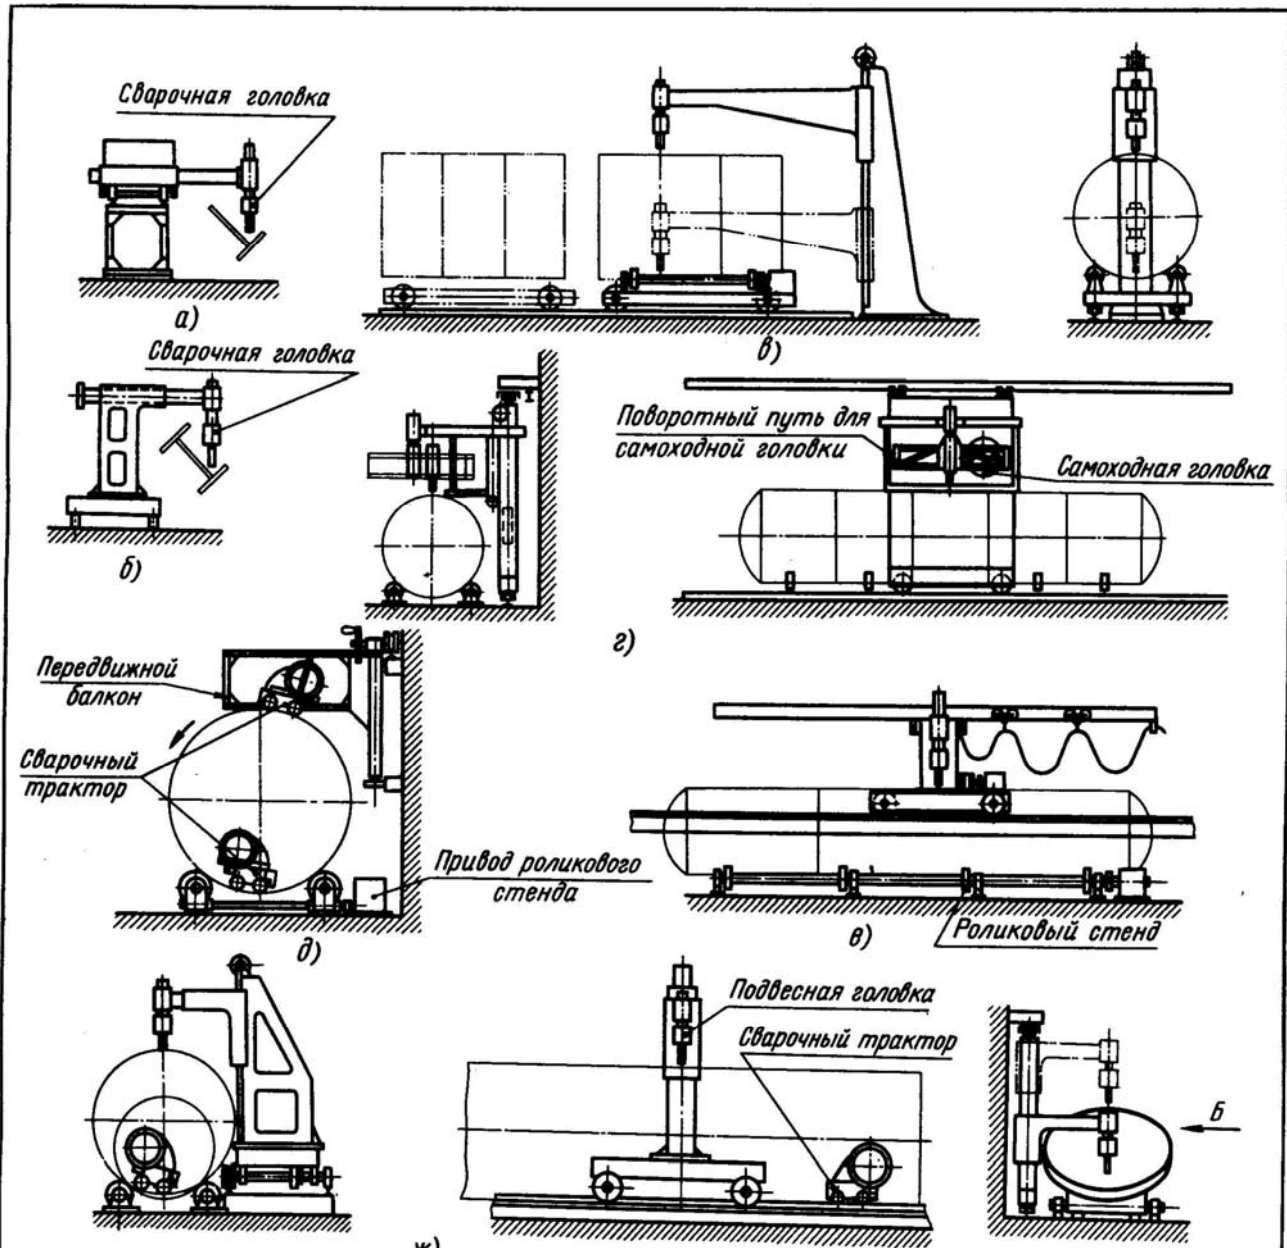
Установки для сварки прямолинейных и кольцевых швов 3500
